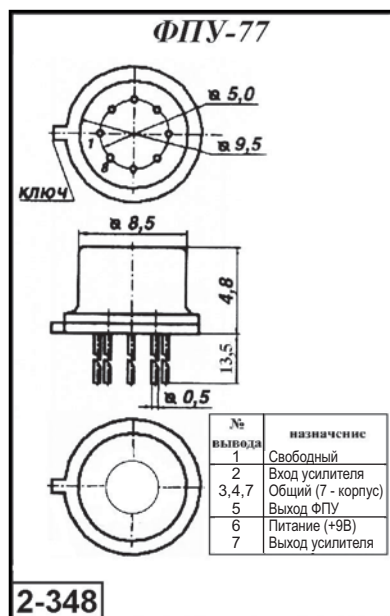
Внешний вид и габаритные размеры ФПУ-77
